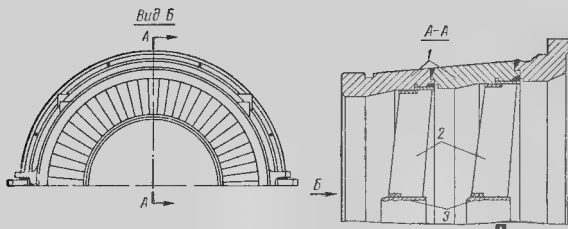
Сварная диафрагма газовой турбины ГТ-25-700:
